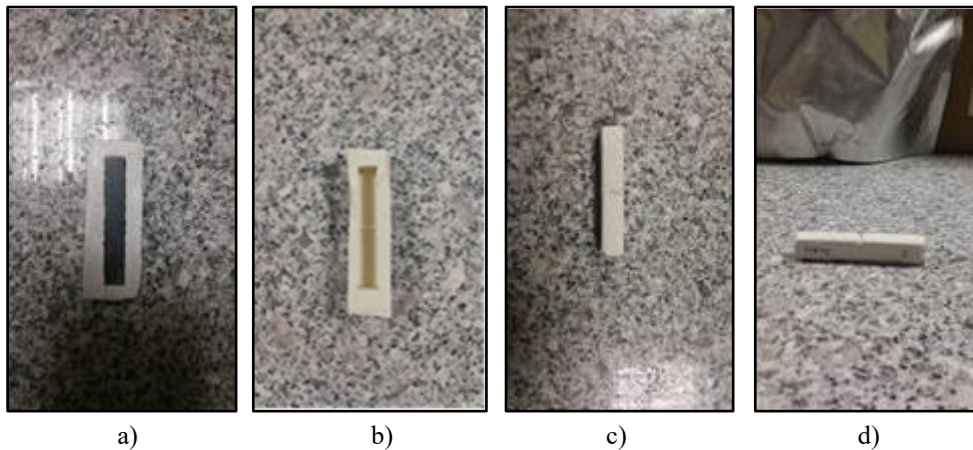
Ensaio de Charpy: a) Molde com provete modelo, b) Molde final; c) e d) Provetes final
